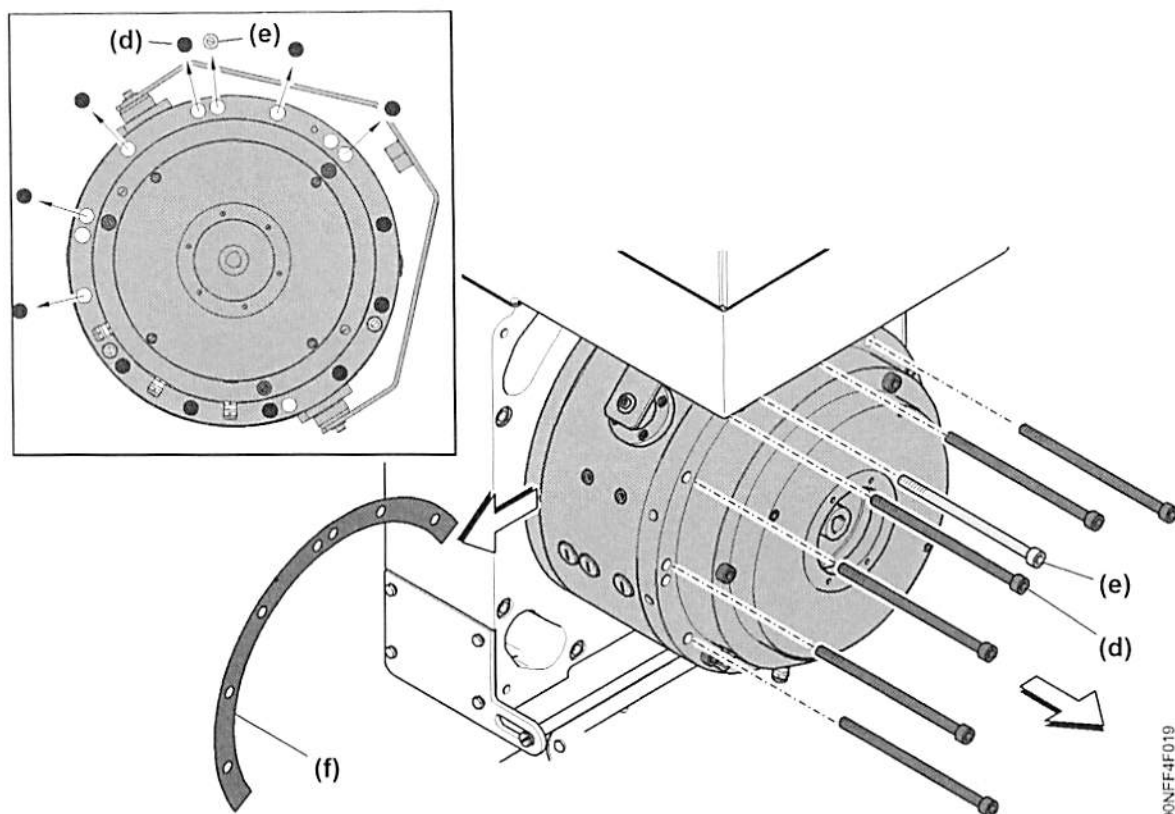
Befestigungsschrauben für Bremsflansch und Bremse demontieren
